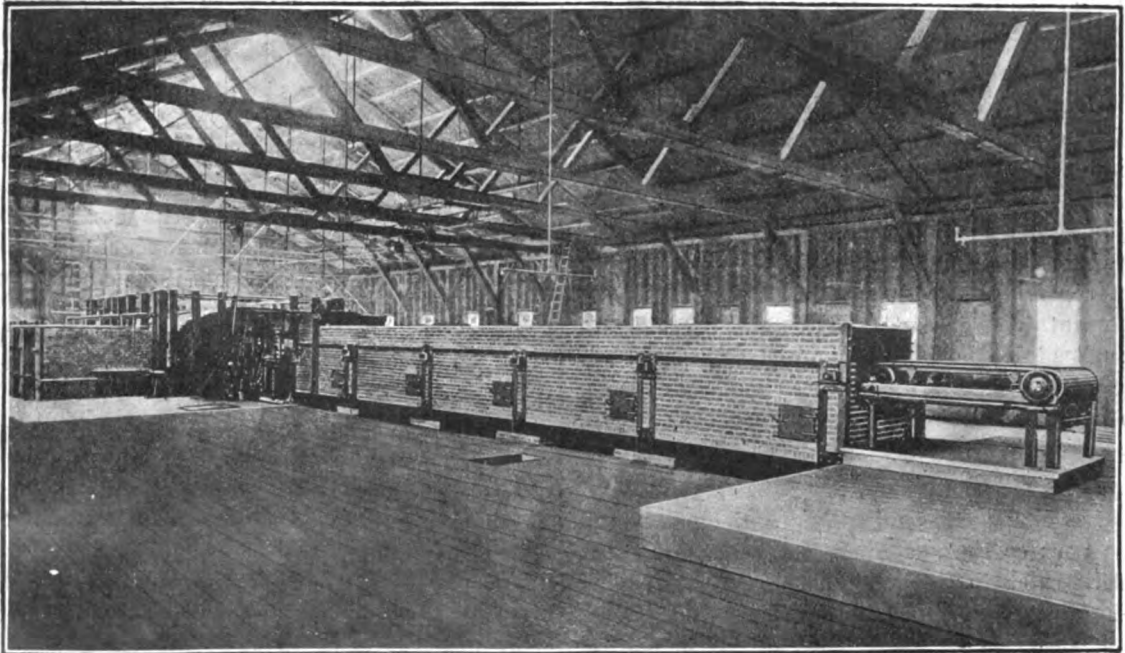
Ensemble de la machine Colburn pour fabriquer le verre à vitre.
